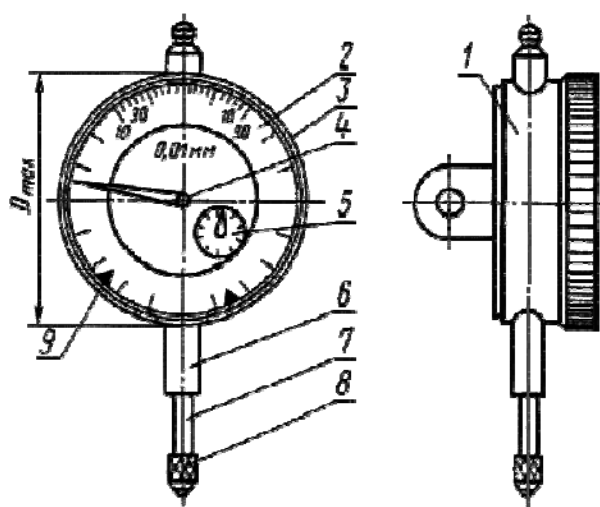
Индикатор типа ИЧ: 1 – корпус; 2 – циферблат; 3 – ободок; 4 – стрелка; 5 – указатель; 6 – гильза; 7 – измерительный стержень; 8 – измерительный наконечник; 9 – указатель поля допуска
